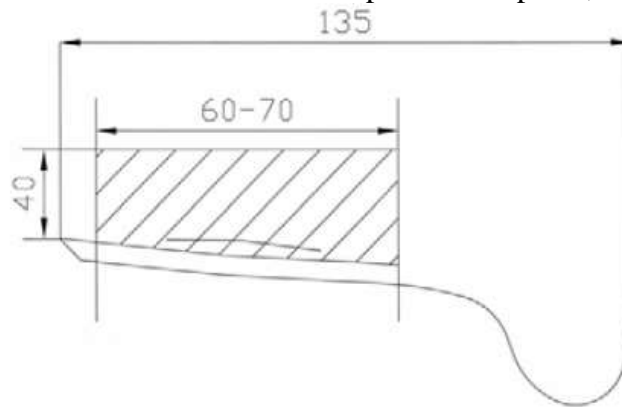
Zona de localización de fisuras circunferenciales en la llanta (medidas en mm).
